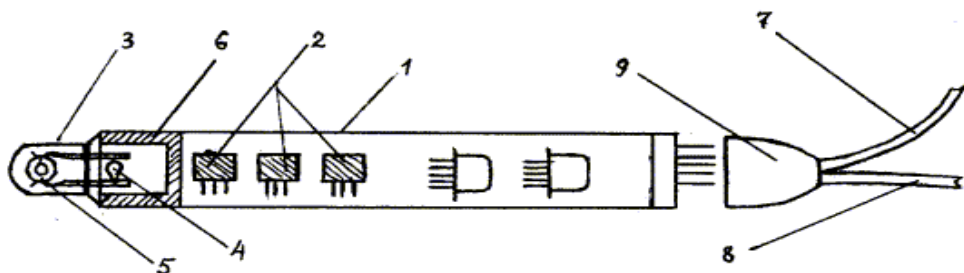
Конструкция датчика Ю.Н.Чередниченко: 1. Алюминиевый корпус; 2. Элементы схемы; 3. Корпус кварцевого резонатора; 4. Термистор; 5. Кварцевый резонатор; 6. Термоизоляция.
